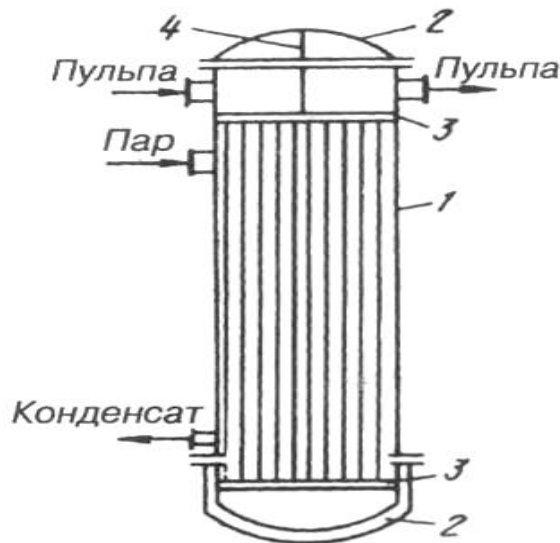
Трубчатый подогреватель: 1 - корпус; 2- крышки; 3- трубные решетки; 4- перегородка
